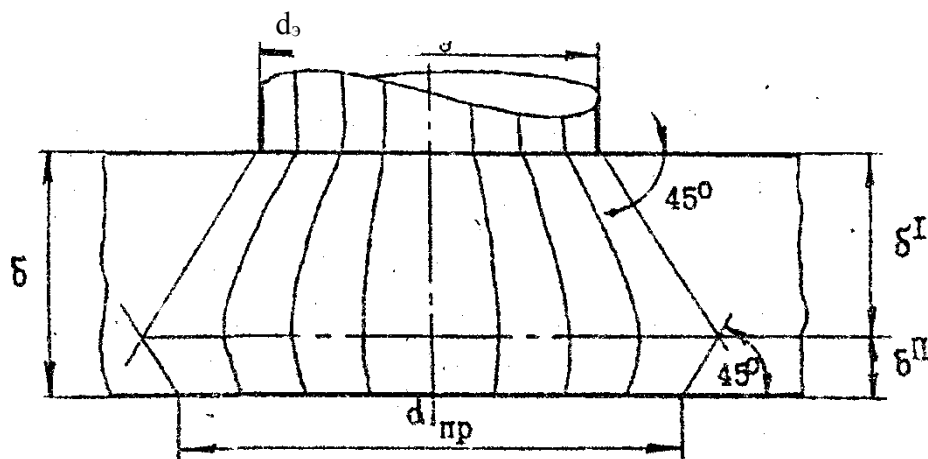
Схема поля тока для расчета сопротивления детали
